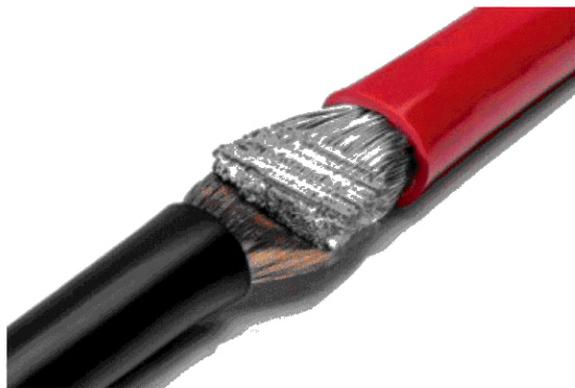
Двустороннее сваривание ультразвуковой сваркой медно-алюминиевое
